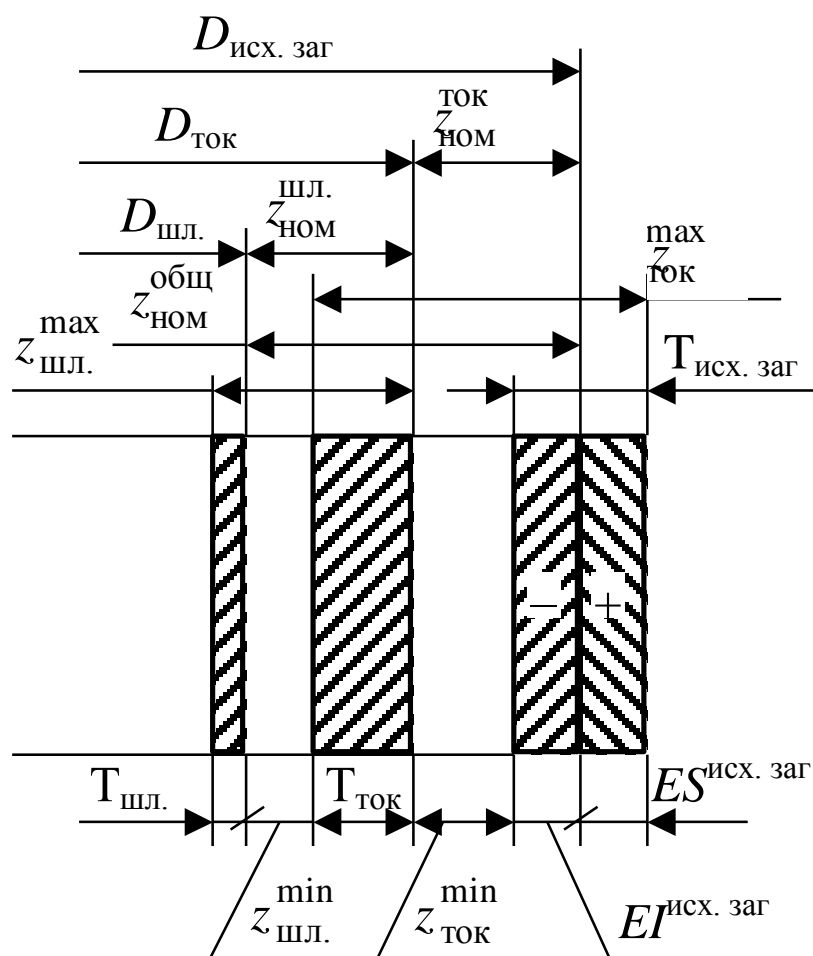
Схема расположения припусков и допусков на токарную обработку и шлифование вала
